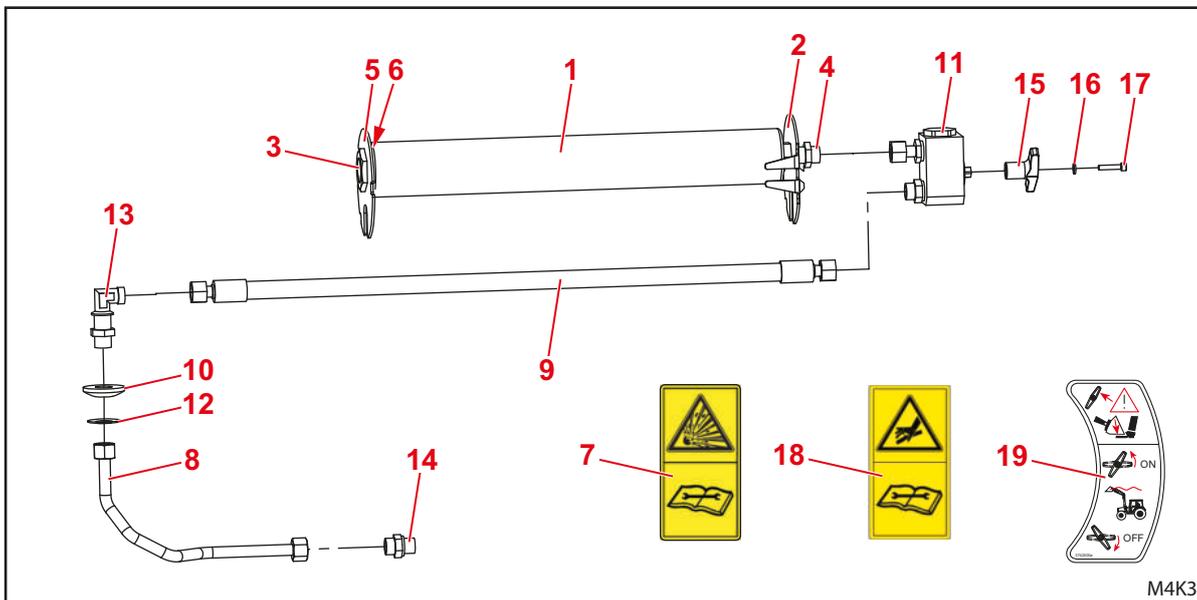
Panoramica equipaggiamento Comfort-Drive
